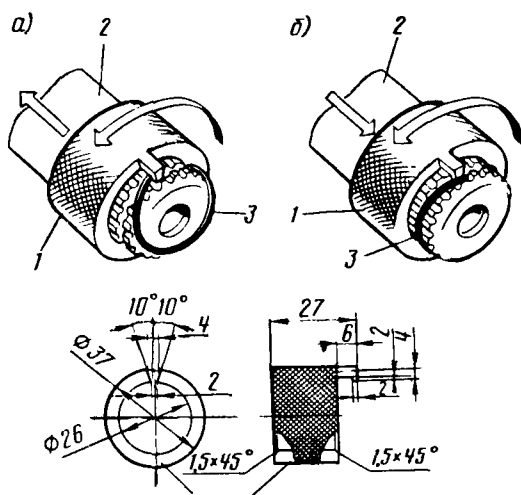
Приспособление для установки (а) и снятия (б) стопорного кольца на внутреннем шарнире шарнирного вала:
